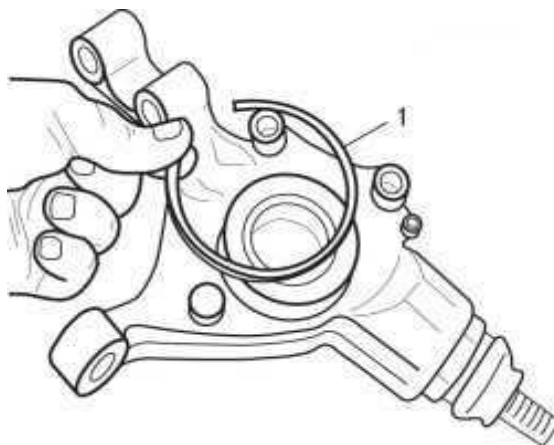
Зняття стопорного кільця підшипника:
